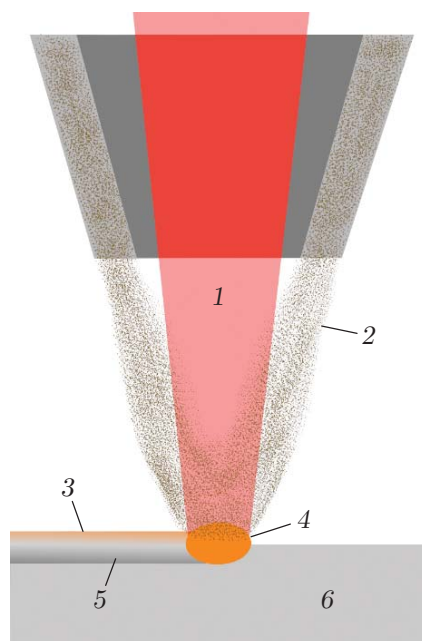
Схема установки для лазерной наплавки (DMD-метод):
